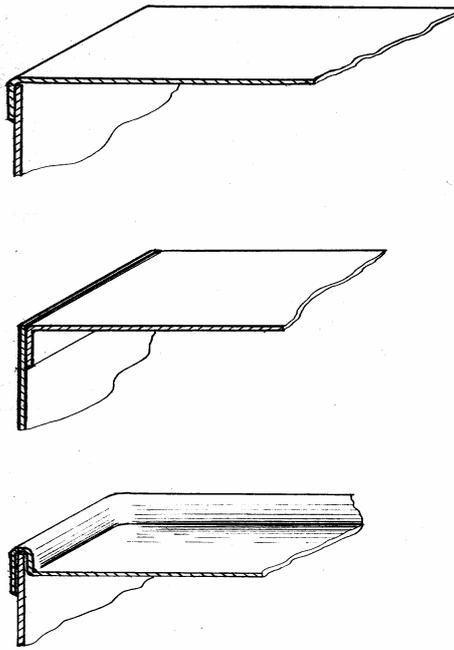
соединение пайкой: 1-“наружная крышка”;
